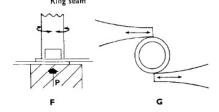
Torsionsschweißprozess (links) und Torsionsschwingungserzeugung (rechts). Quelle: E.A. Neppiras, "Ultrasonic Welding of Metals", Ultrasonics (1965)
